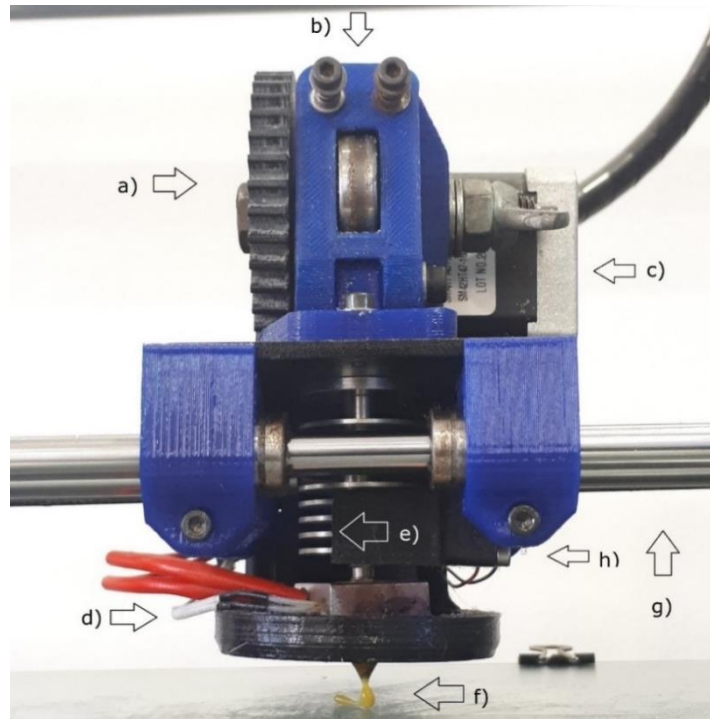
Partes que componen el cabezal de una máquina 3D+ a) engranes b) entrada de filamento c) motor d) bloque calentador e) dissipador de calor f) boquilla g) barras de movimiento h) ventilador de refrigeración. Fuente: Elaboración propia.
